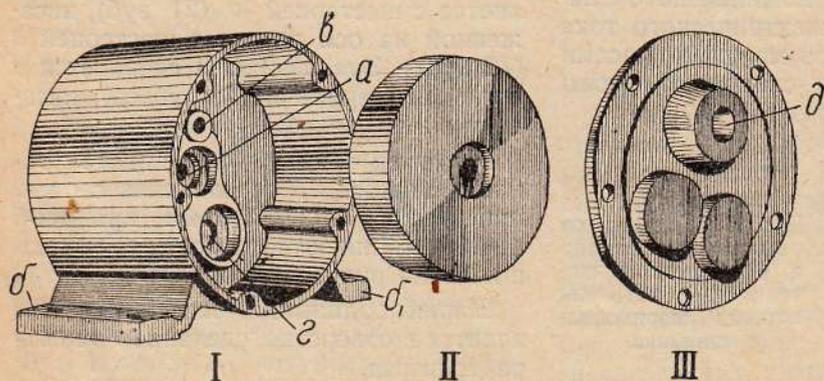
Корпус механической части динамопривода ГОЗ. I — корпус; II — маховик, насаживающийся на ось якоря; III — крышка корпуса; а — отверстие для оси якоря; б, б₁ — основание корпуса; в — подшипник для главной оси; г — отверстие для шарикоподшипника промежуточной оси; д — подшипник в крышке корпуса для главной оси
